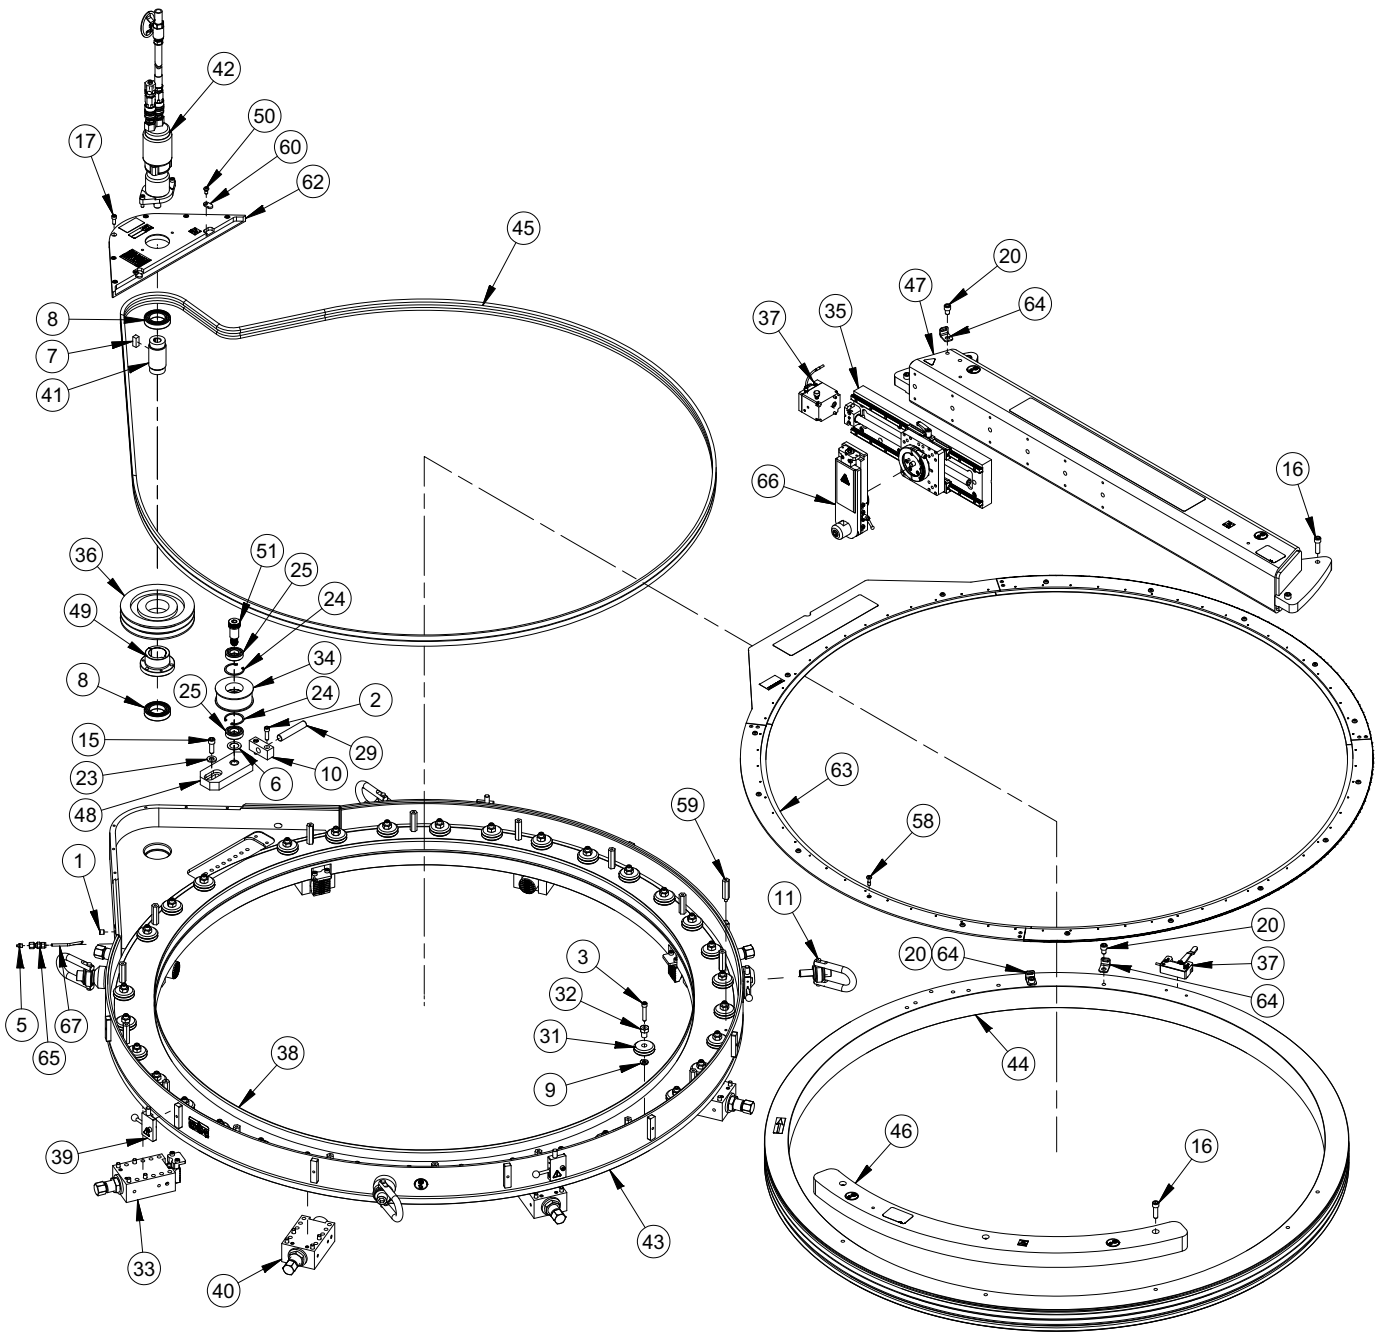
CONJUNTO DEL ODF60 SPEED FACER (N/P 86990)
